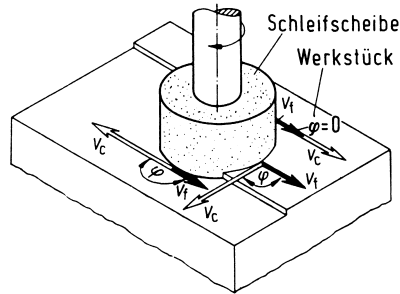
Vorschubrichtungswinkel φ beim Schleifen mit Stirnfräser (nach DIN 6580)
